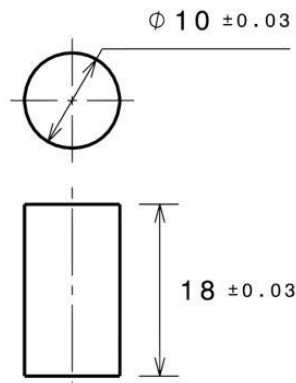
Dimensiones de las probetas en TU Freiberg (mm)
